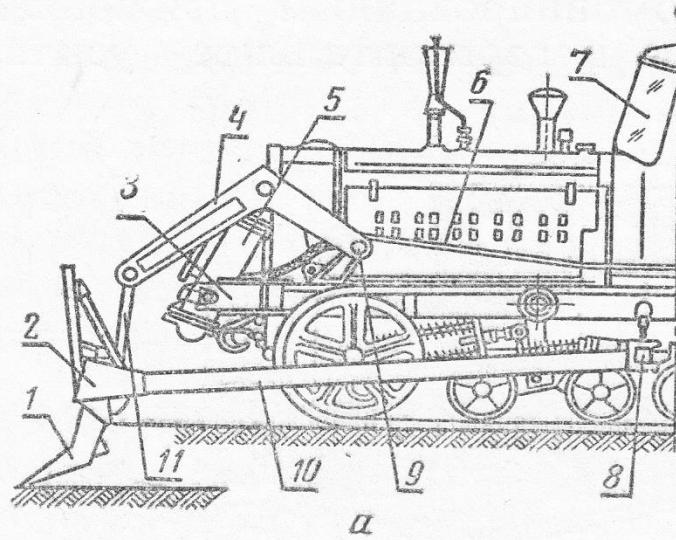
Общий вид корчевателя-собирателя с передними подъемными гидроцилиндрами.
